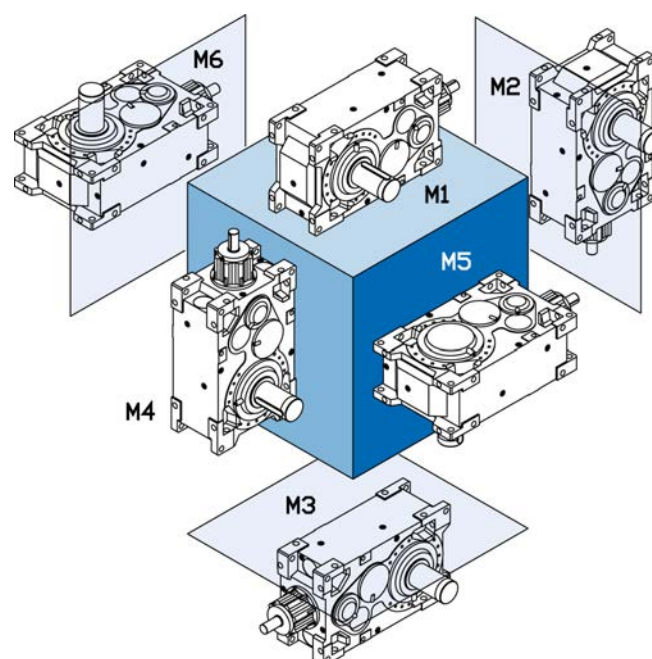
Монтажные положения конических редукторов со стандартными монтажными поверхностями
